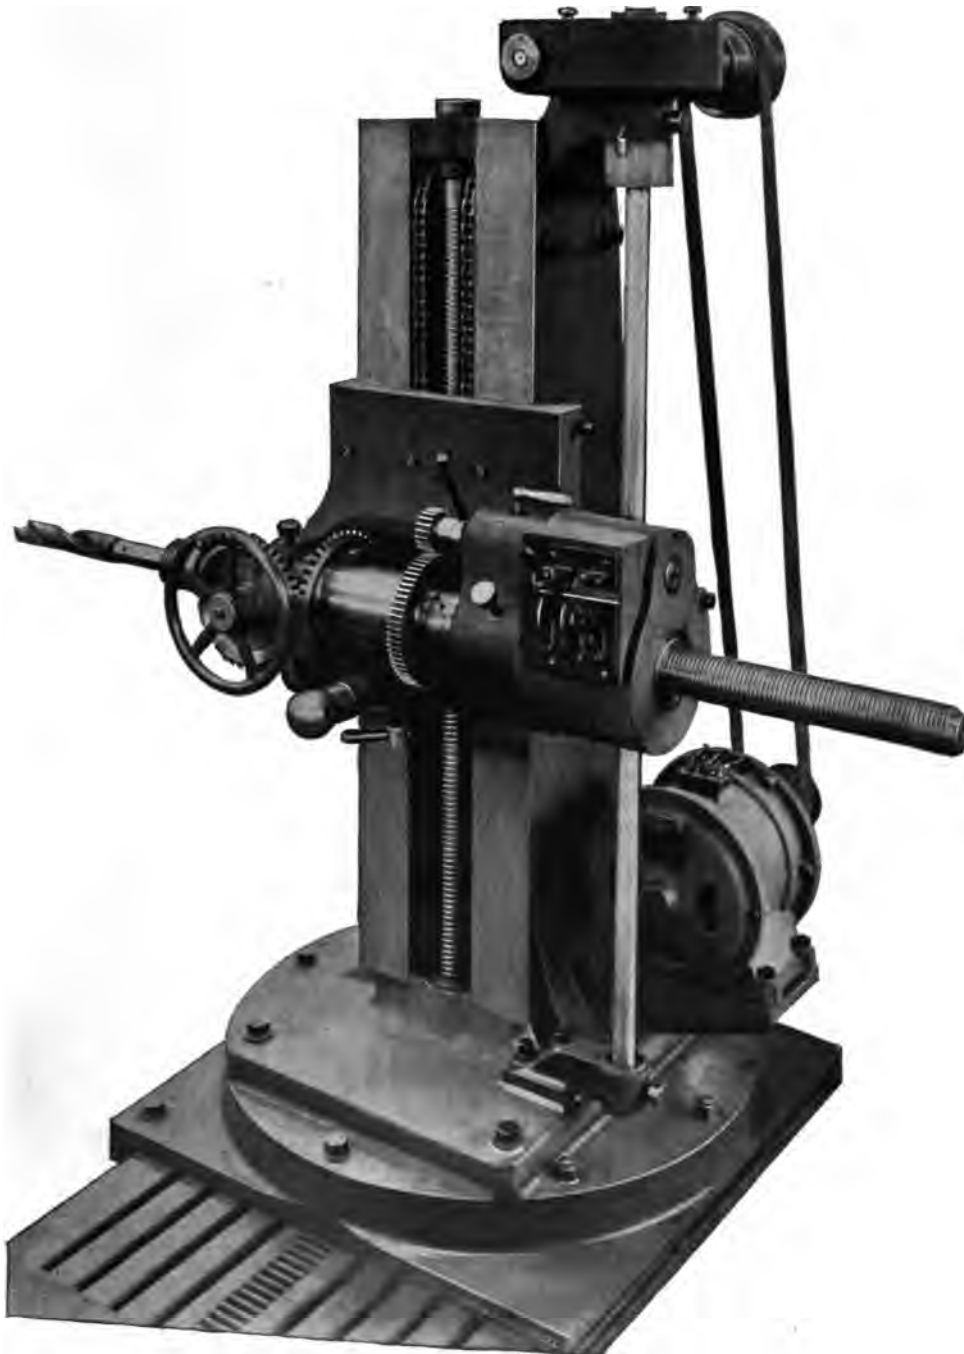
Horizontalbohr- und Fräsmaschine (Maschinenfabrik Oerlikon).
